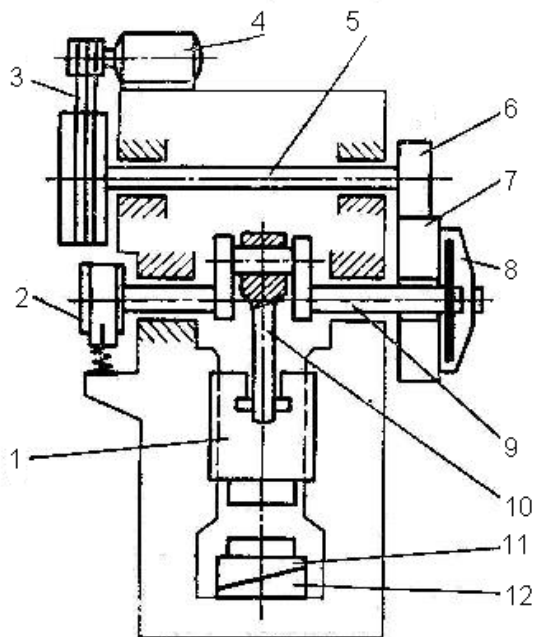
Кинематическая схема кривошипного горяче-штамповочного прессы
